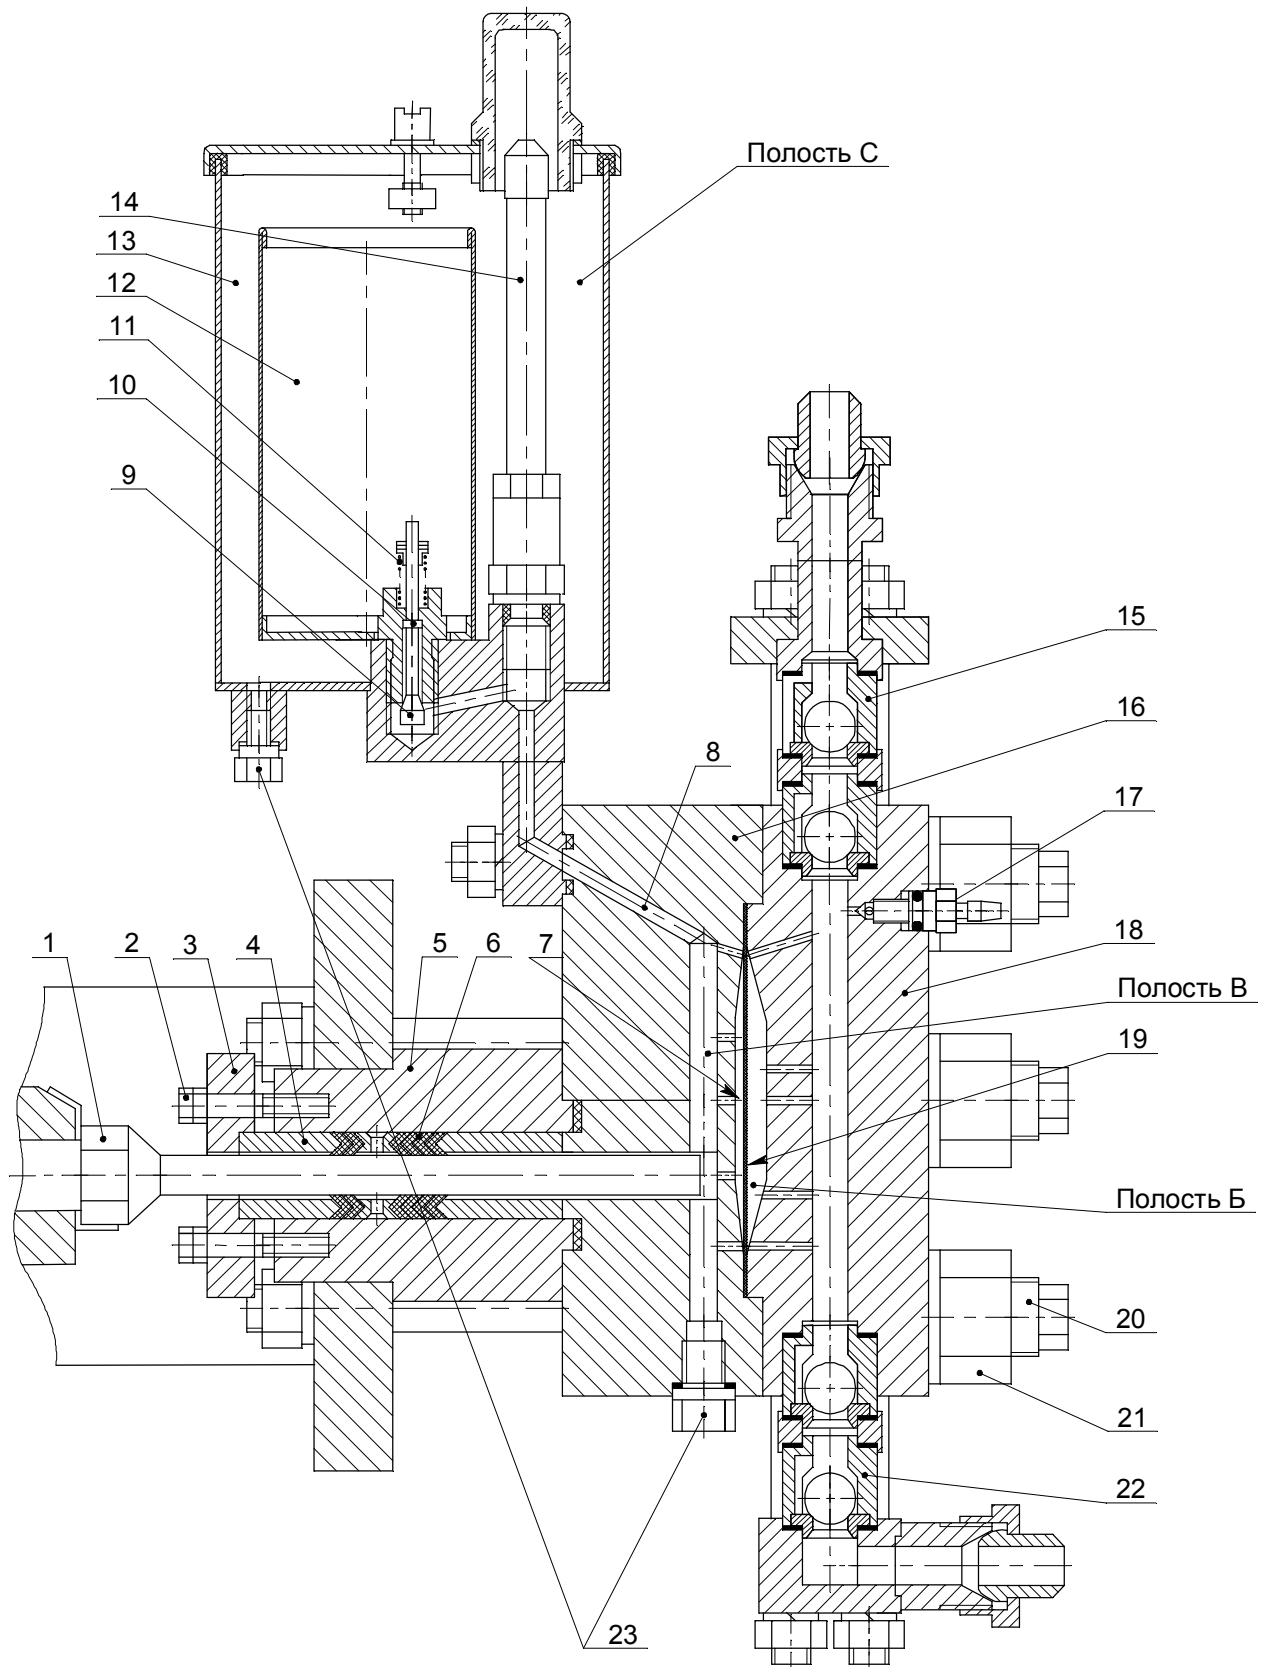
Конструкция мембранной головки агрегата с параметрами номинального режима 16/63; 25/250; 40/40; 40/160; 63/100 и 100/250
